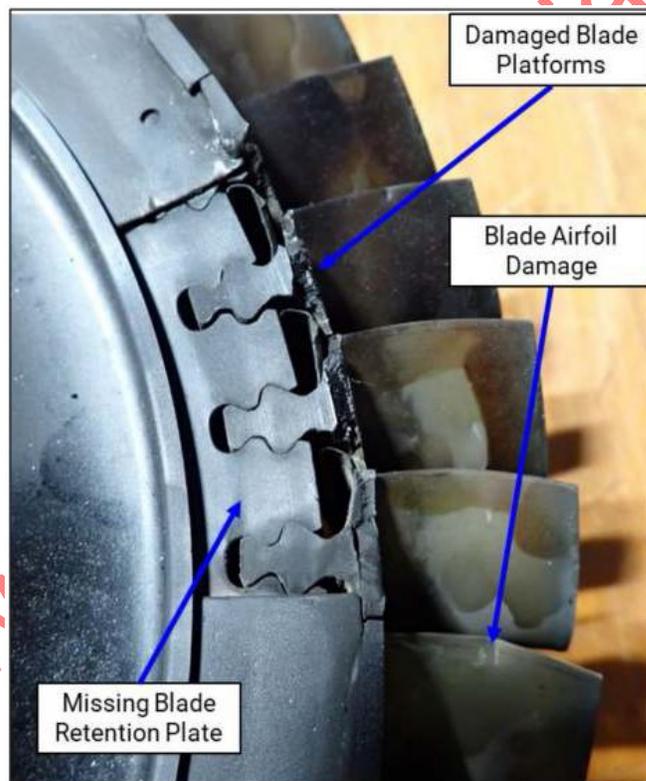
Vista trasera del conjunto de rotor de turbina de alta presión
